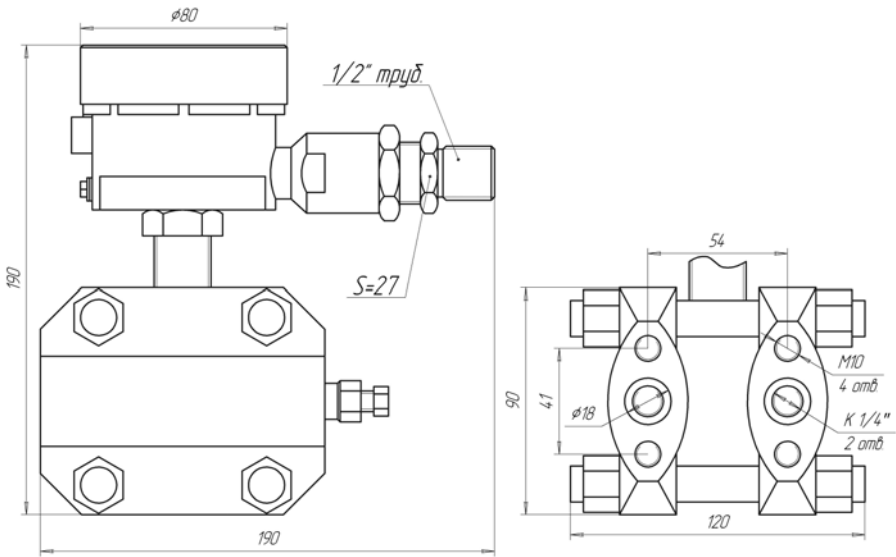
Модель 1167. Взрывозащита, стальной корпус, ввод под трубу.
